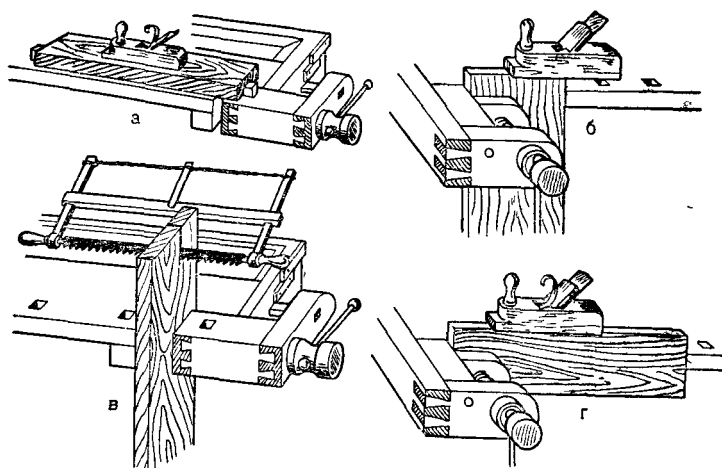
Зажим обрабатываемых изделий в верстаке:
